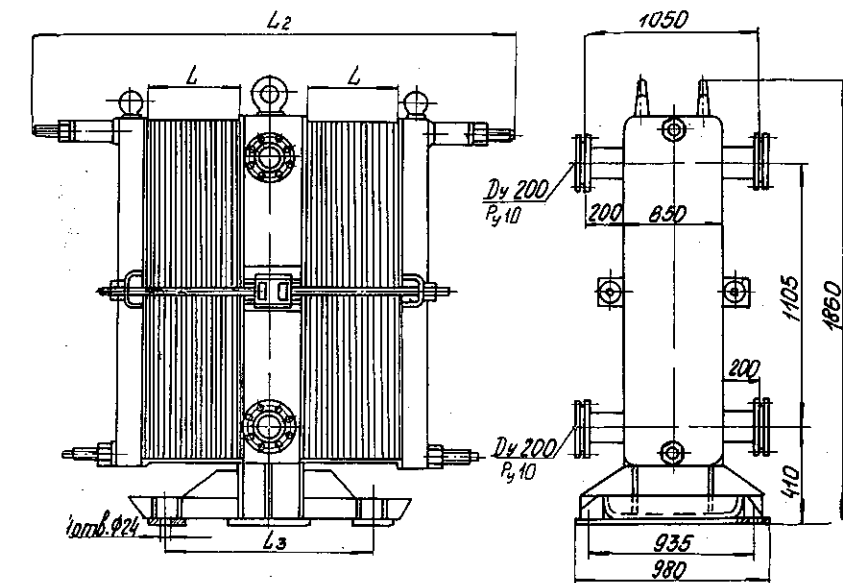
Общий вид конденсатора с габаритными и присоединительными размерами (исполнение IV-A)
